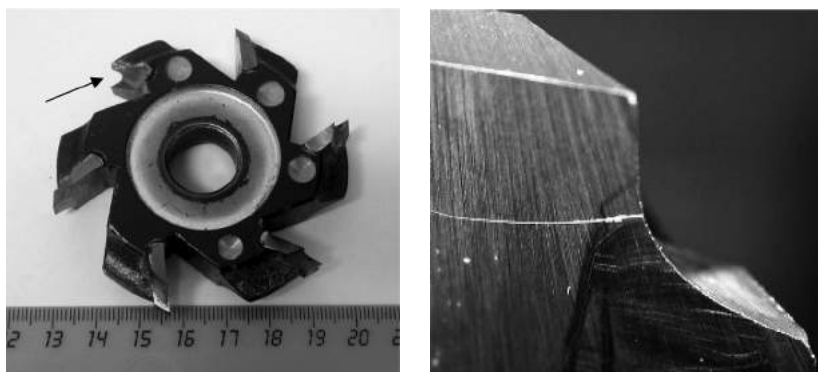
Макроструктура сварного соединения:
